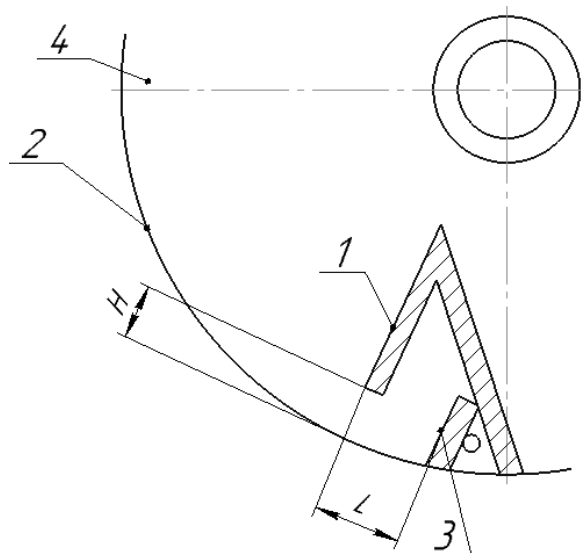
Положення лопатей в зоні завантаження комірки барабана 1 – нерухома лопать; 2 – обичайка металника; 3 – рухлива лопать; 4 – диск барабана.
